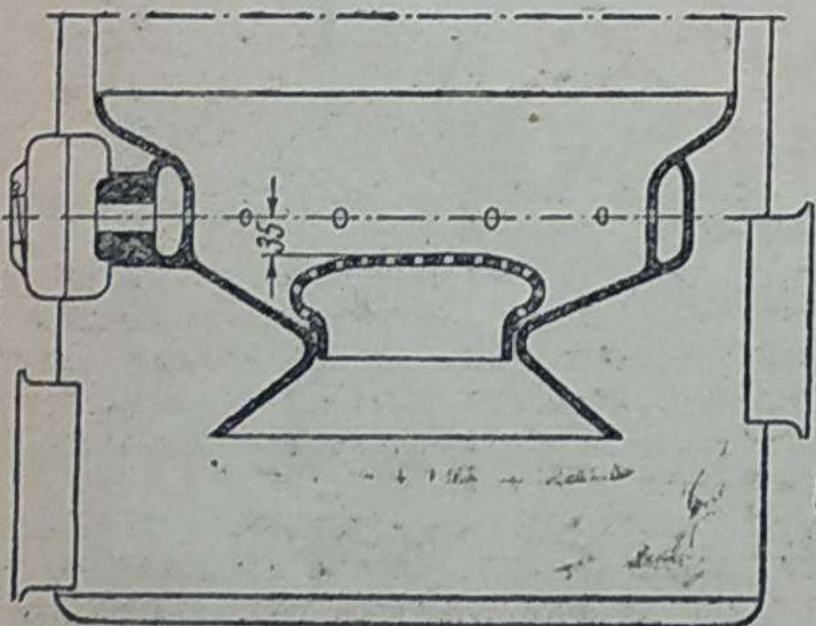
Схема газогенератора ЗИС-21 с решеткой Ротмистрова.
